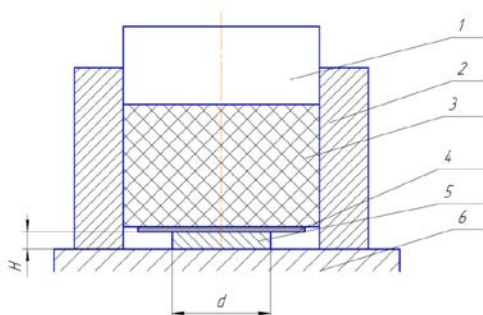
Схема вырубki жёстким шаблоном. 1 – верхний боёк; 2 – бандаж; 3 – эластичная матрица; 4 – листовая заготовка; 5 – шаблон; 6 – нижний боёк.
